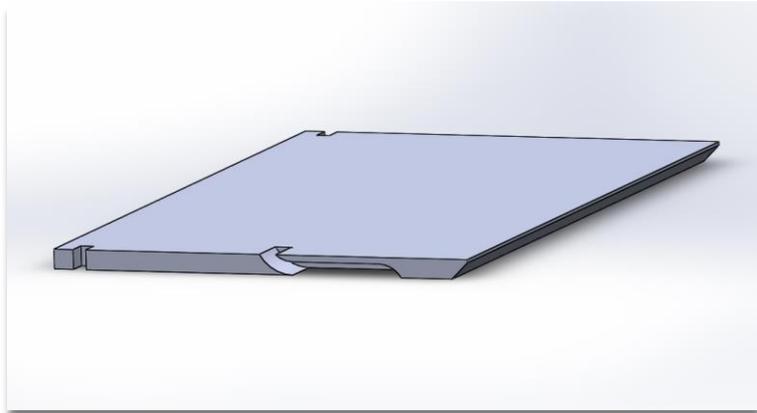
Ranura delantera para machihembrado de la pata izquierda.
